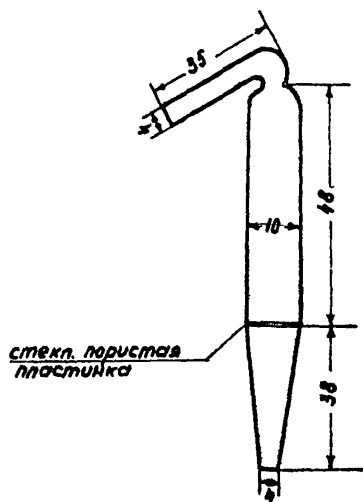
Стеклянная трубка с пористой пластинкой для отбора проб воздуха
